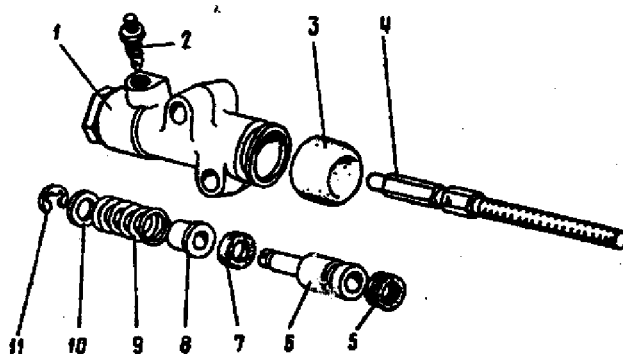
Componentes do cilindro atuador: 1 - corpo; 2 - sangrador; 3 - coifa; 4 - haste de acionamento; 5 - gaxeta; 6 - êmbolo; 7 - anel de vedação; 8 - prato; 9 - mola; 10 - arruela; 11 - anel de retenção.
